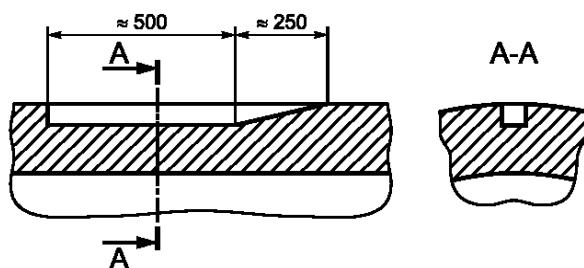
Канавка, обрабатываемая на наружной поверхности трубы
